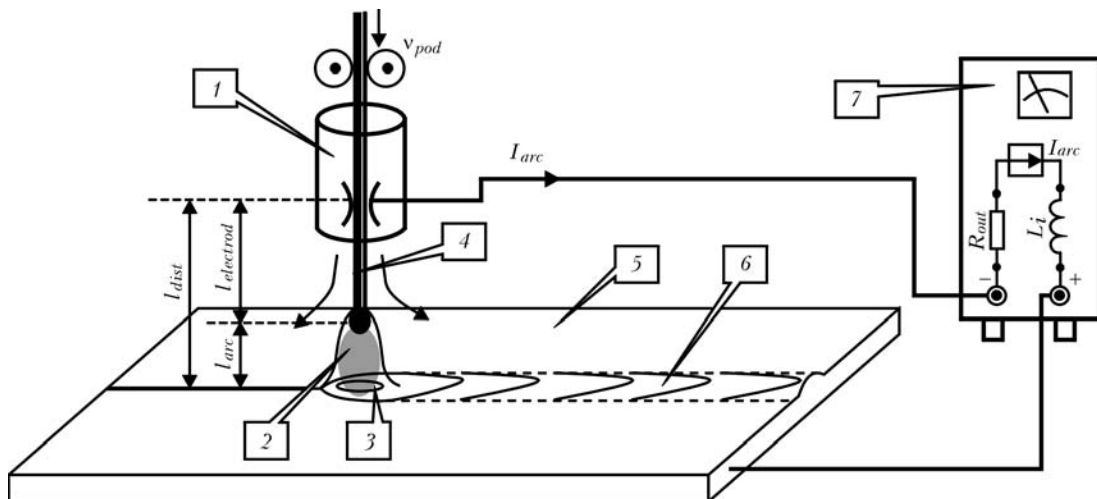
Схема сварки МИГ: 1 — горелка; 2 — дуга; 3 — сварочная ванна; 4 — вылет электрода; 5 — изделие; 6 — сварной шов; 7 — источник питания дуги
